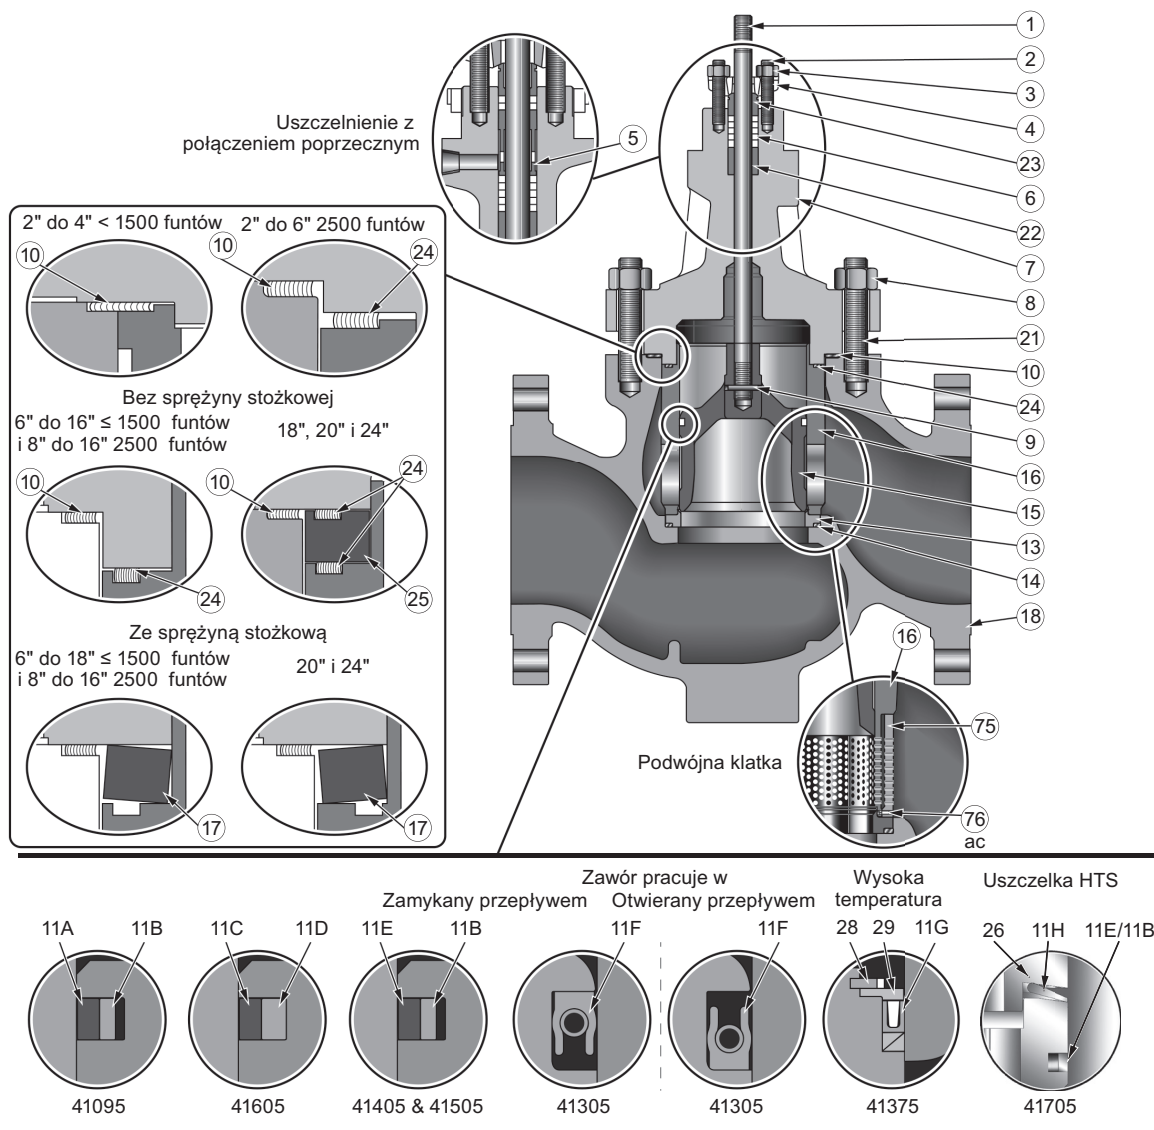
Części wewnętrzne zaworu pilotowego – typ 41405
